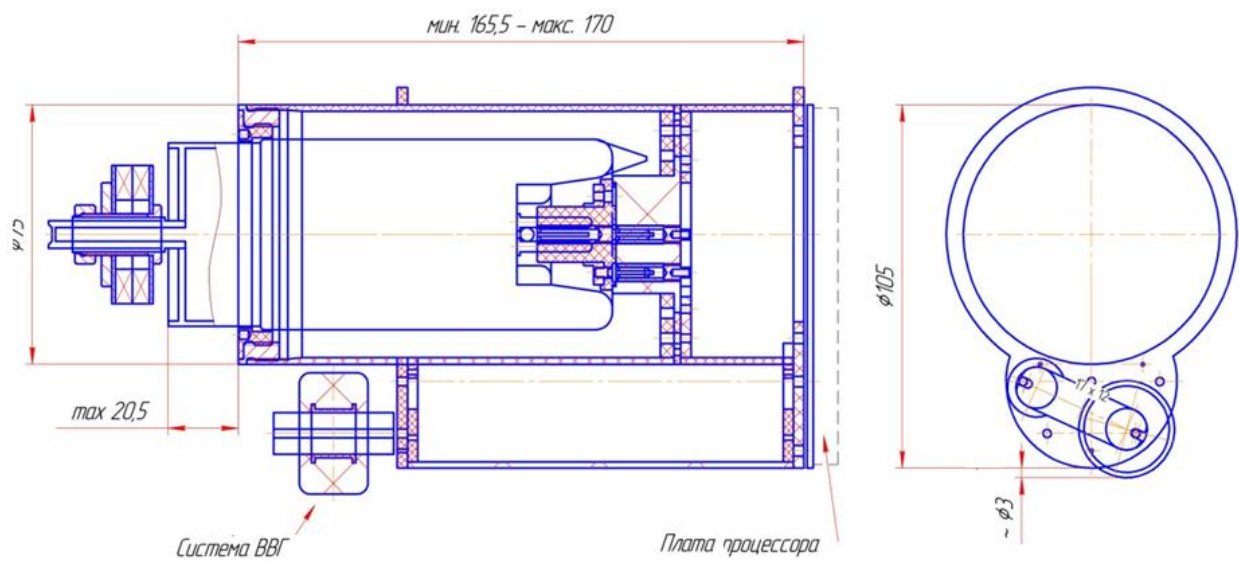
Конструкция излучателя (без корпуса) аппарата «ПАРДУС-Р»
